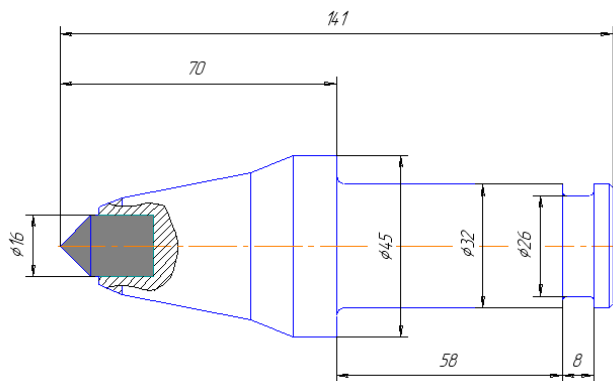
Тангенциальный поворотный резец РШ 32-70/16 с цилиндрической твердосплавной вставкой
